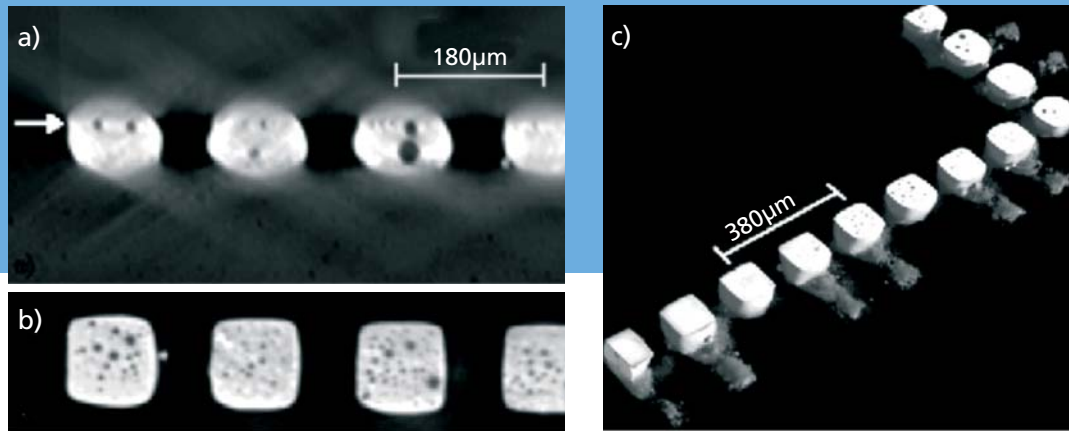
Visualización no destructiva de las soldaduras de un chip con la placa en la que se aloja. Cortes transversales (a) perpendicular y (b) paralelo a la superficie del dispositivo. (c) Vista 3D: las 9 soldaduras en fila abarcan 1 mm.
